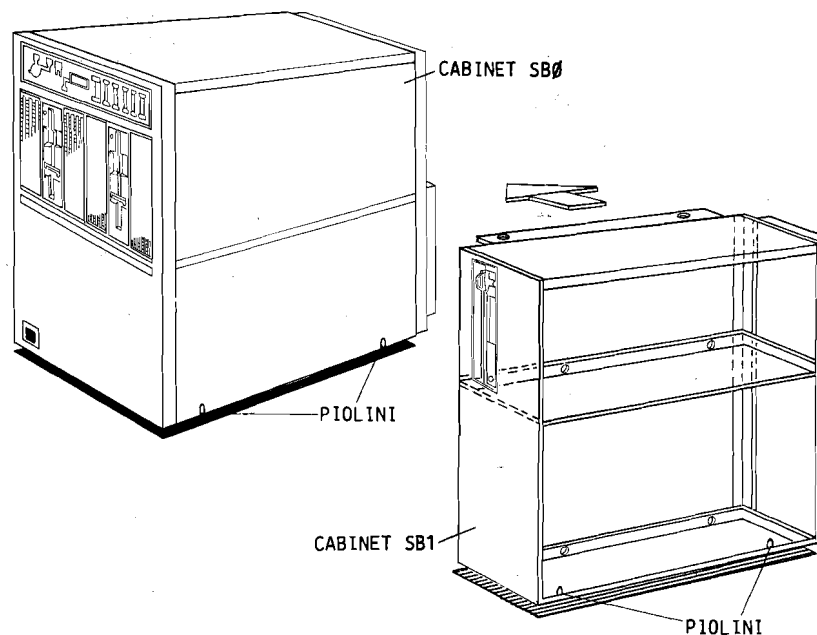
Viste anteriore delle strutture SB0 e SB1
